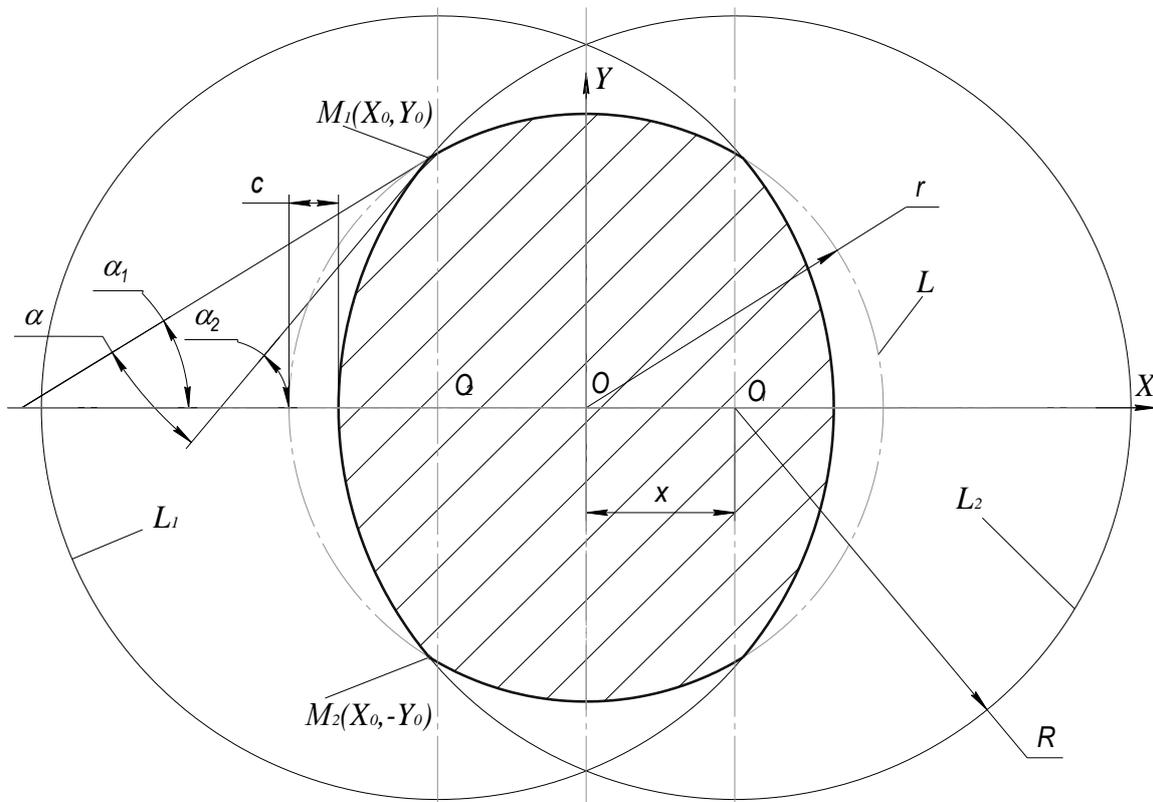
Схема получения профильного вала с двумя круговыми моментопередающими участками
